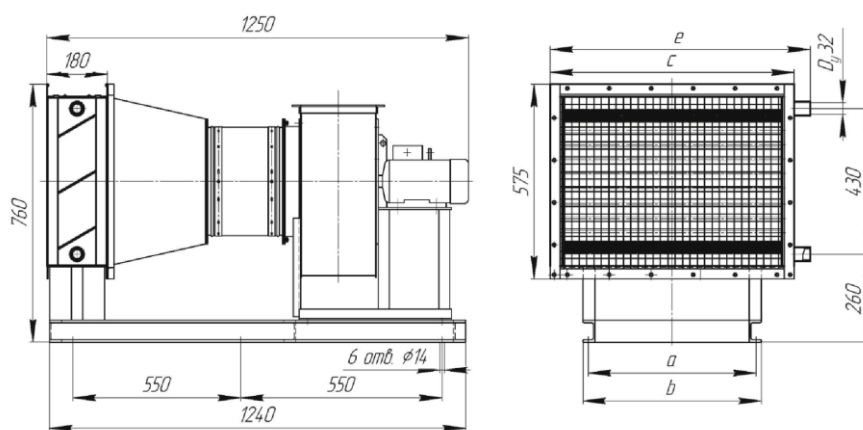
Габаритные и присоединительные размеры воздушнонагревательных установок ВНУ.
